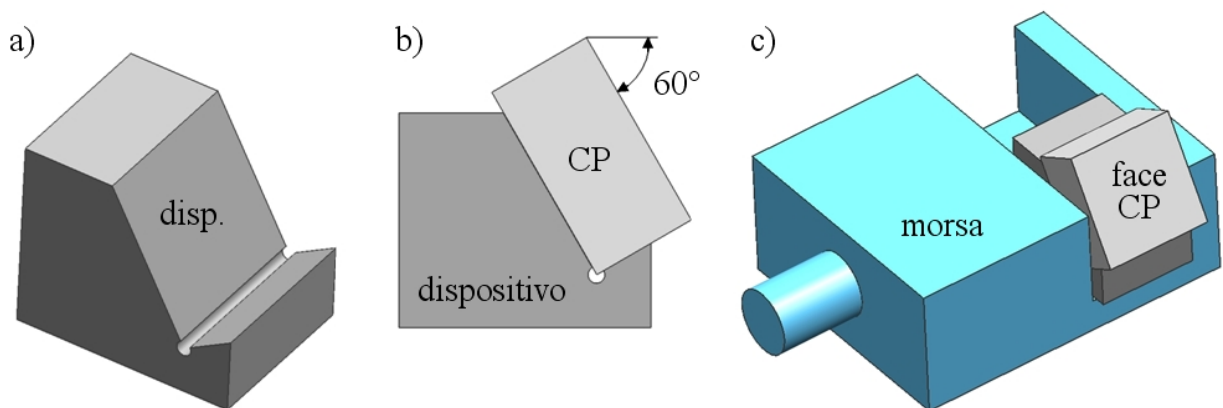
Fixação do corpo-de-prova: a) dispositivo de plano inclinado; b) CP assentado no dispositivo; c) CP fixado na morsa mecânica
